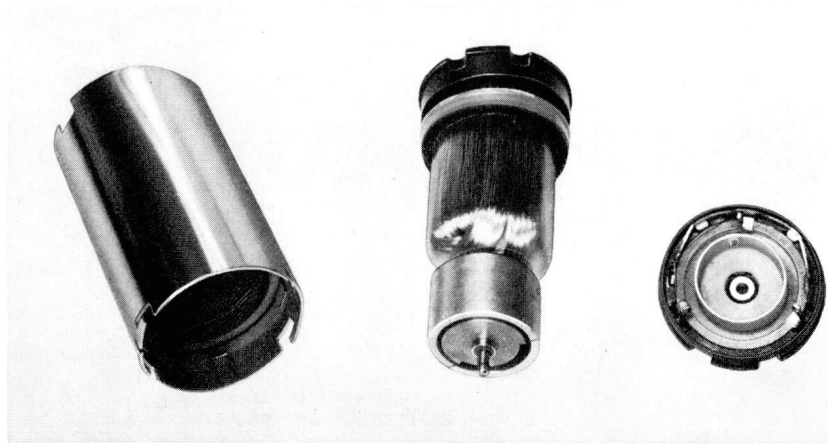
Aufbau des feldplattengesteuerten, kollektorlosen Gleichstrommotors, (links: Dynamoblechmantel im Metallrohr, Mitte: Wicklung und Steuerkopf, rechts: Feldplatten mit Anschlüssen)
